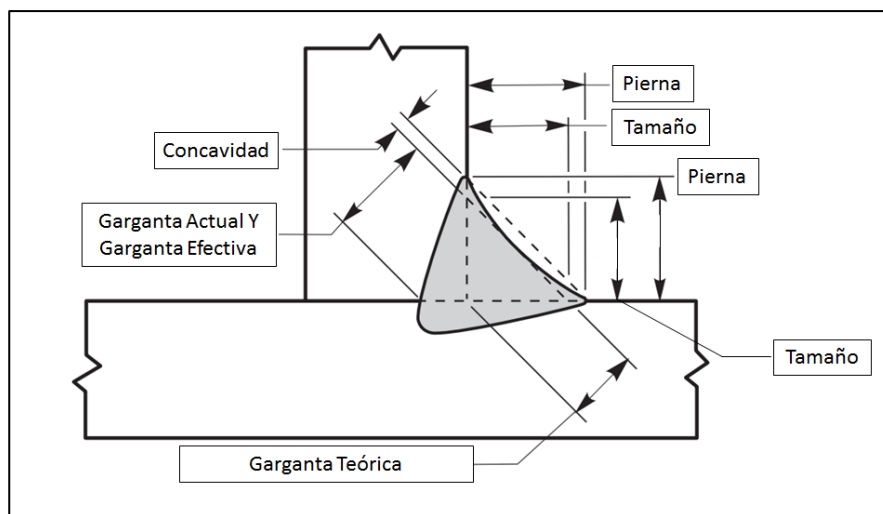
Soldadura De Filete Cóncava [11].
